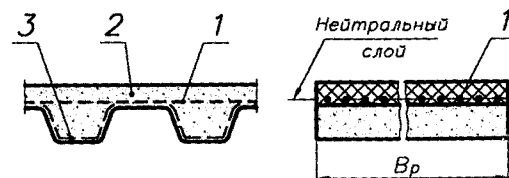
Конструкция зубчатого ремня с трапецидальными зубьями: 1 - кордшнур (металлокорд или углеродное волокно); 2 - тело ремня (маслостойкая резина, пластмасса); 3 - тканевая обкладка (для ремней, изготавливаемых методом прессования)
